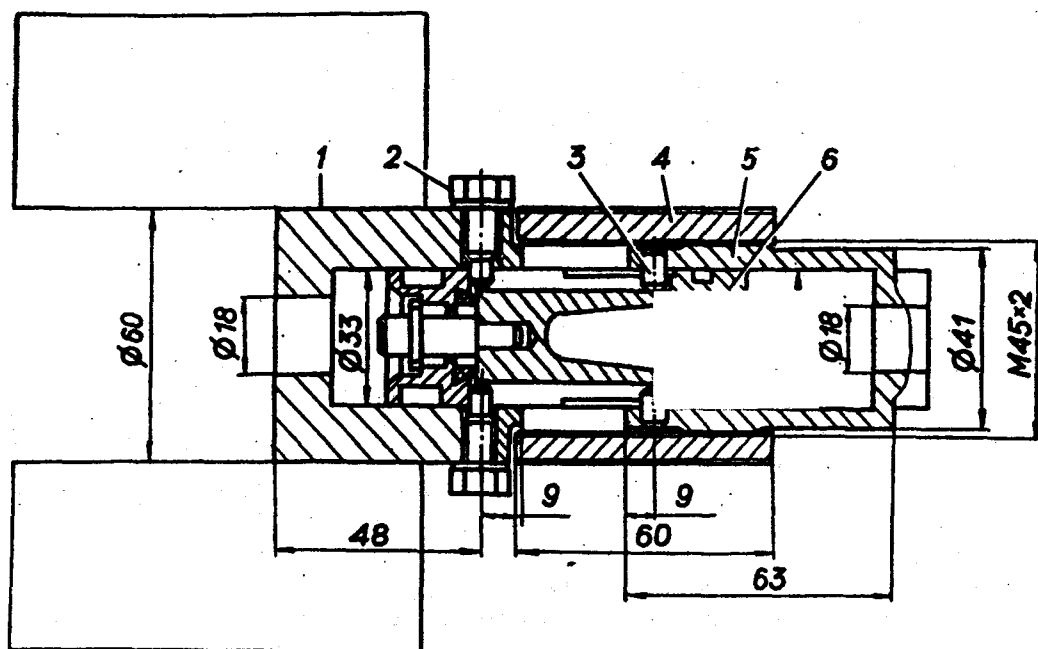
Разборка поршня главного тормозного цилиндра:
